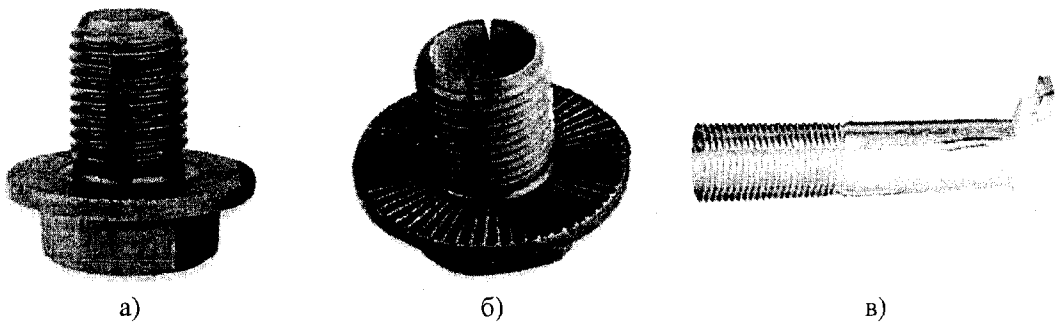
Повреждения резьбы из-за дефектов в исходном металлопрокате: а) рванины или выкрашивание по профилю; б) разрушения при накатке и эксплуатации; в) трещины на головке и на стержне болта
